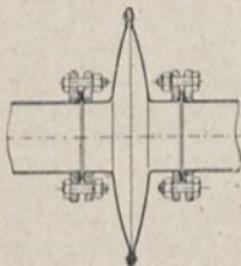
Plattenkompensator mit plattenförmig ausgebildeten Federn.
